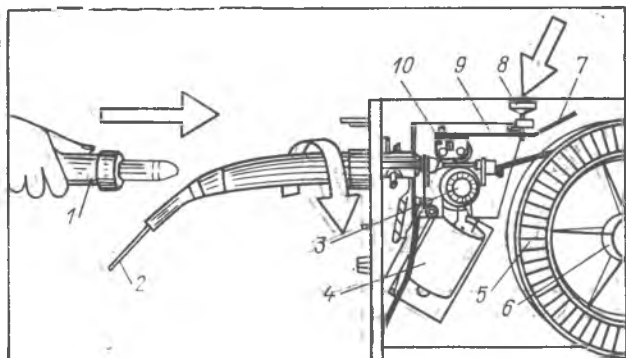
Сварочная горелка для полуавтоматической сварки в защитном газе
